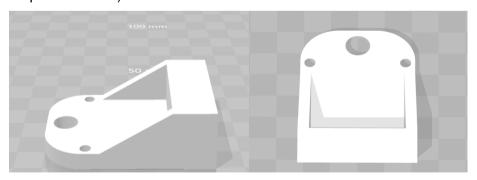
Haste com suporte para motor de passo 02 (vistas frontal e superior, respectivamente)
